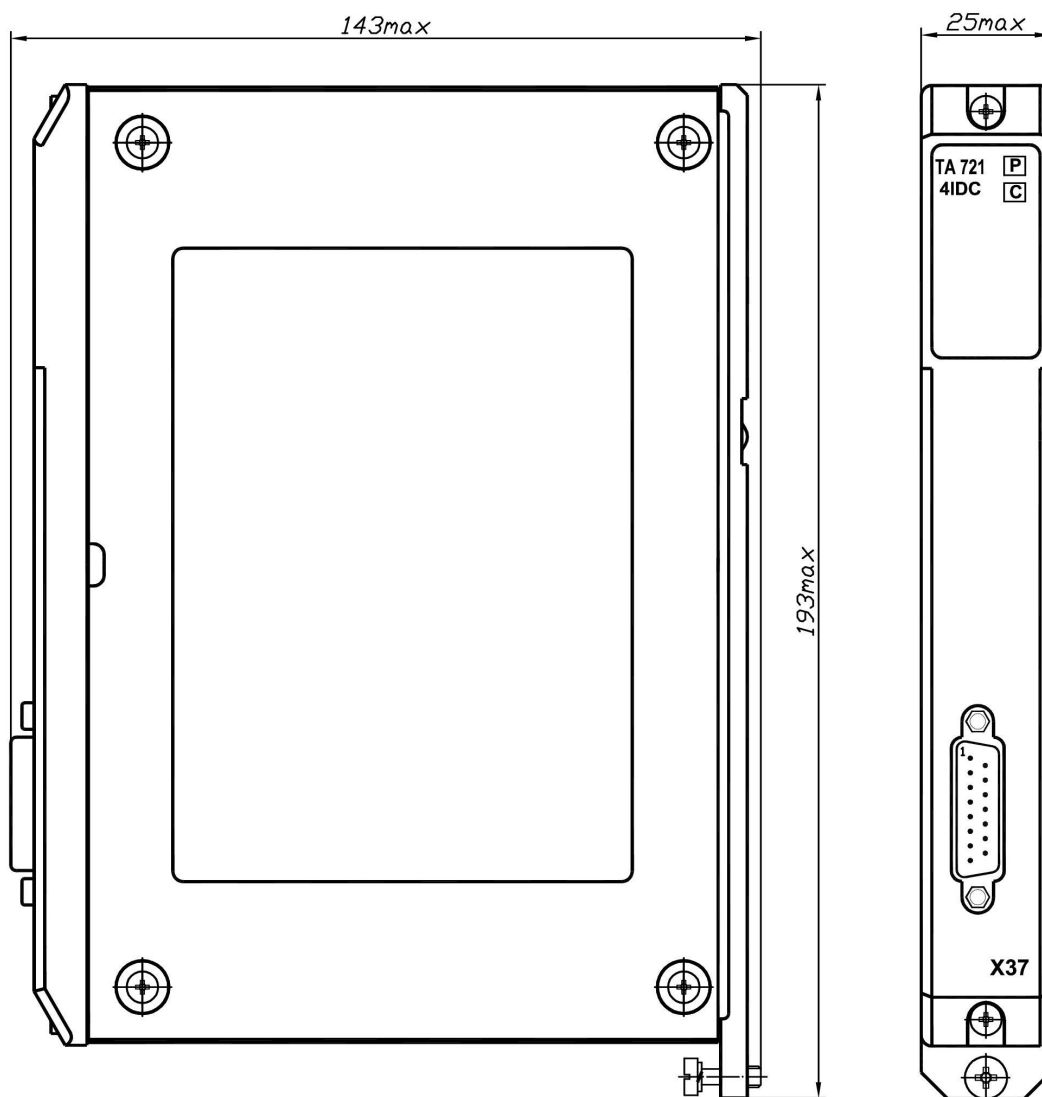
Внешний вид и габаритные размеры модуля исполнения TA 721 4IDC
